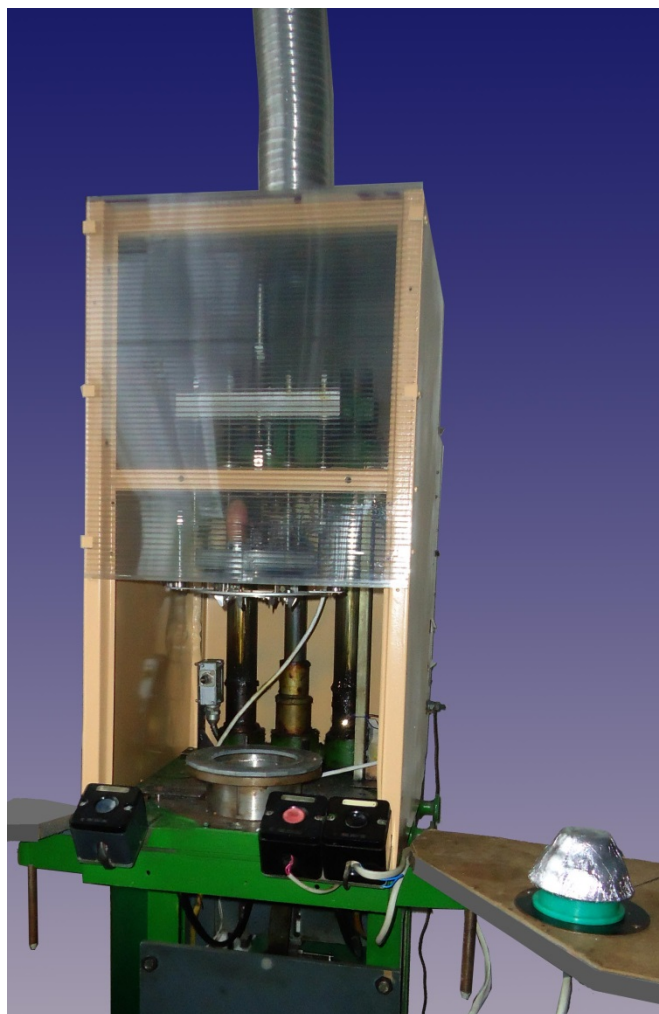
Установа для зварювання кромки корпусу півмаски
